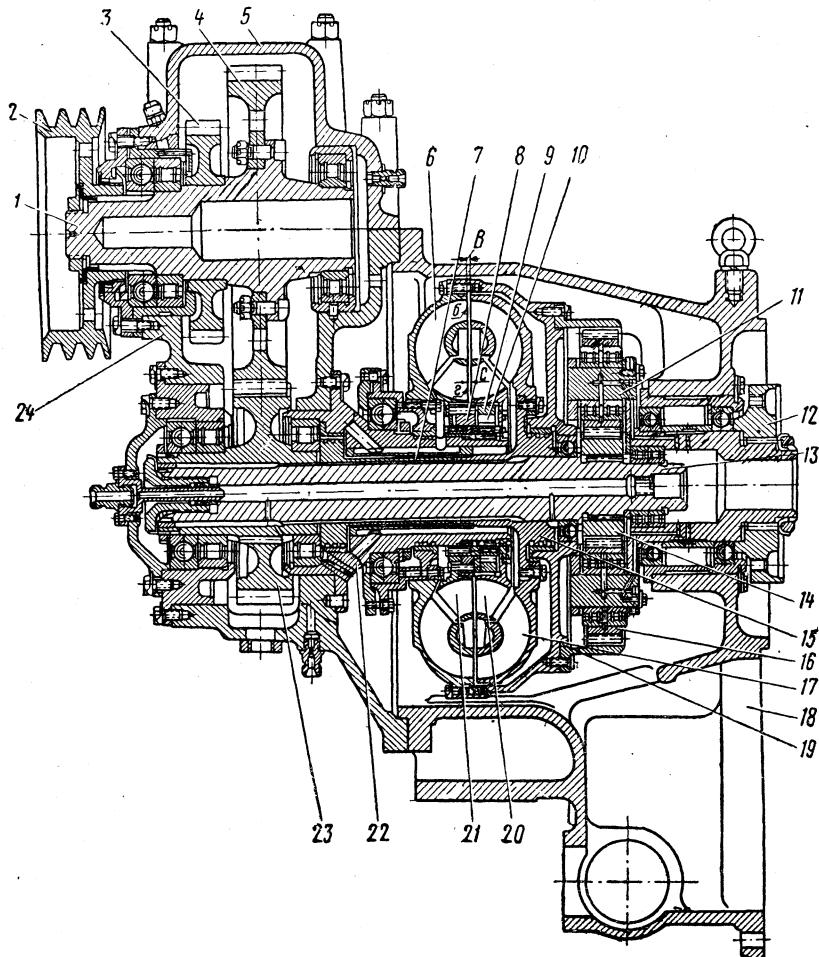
Гидромеханический трансформатор с повышающим редуктором:
